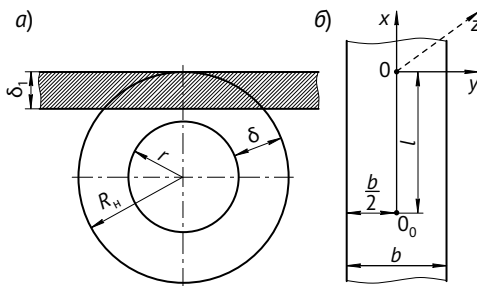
Схема развертки цилиндрической детали в бесконечную пластины (а) и движения источника тепла (б)
